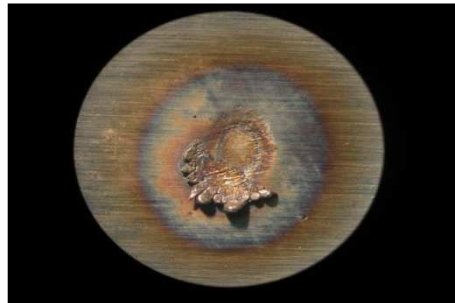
7. Punto de soldadura en la probeta de 1.5 mm a 5x.
